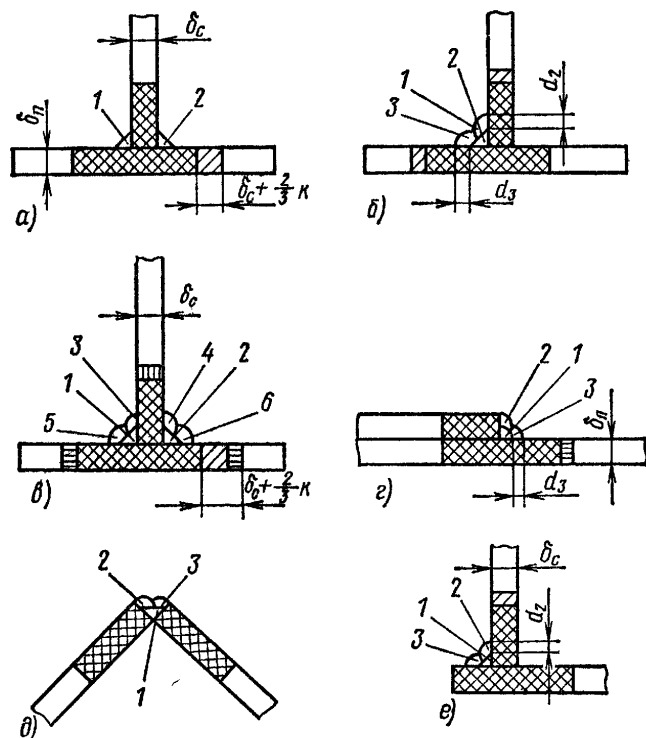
Сварные соединения в балочных конструкциях: 1—6 — валики (зоны пластических деформаций заштрихованы)
